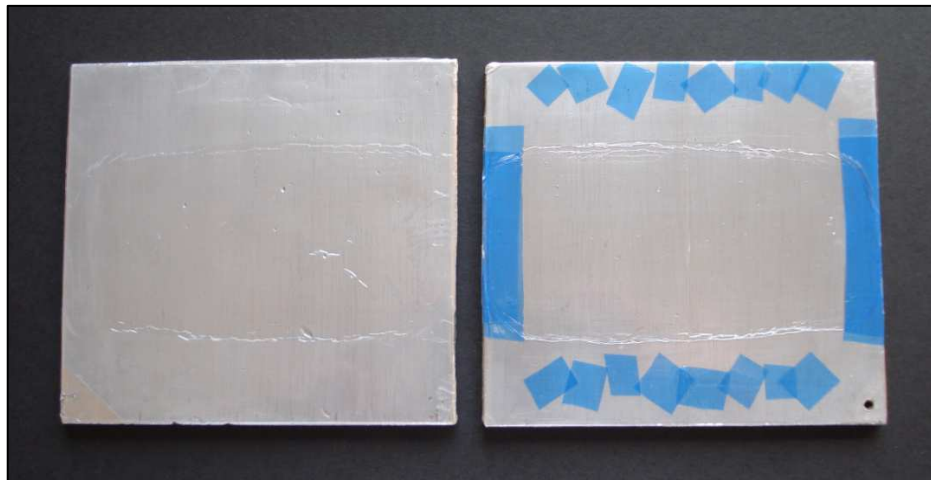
Aperture delle piastre dopo lo stampaggio per compressione
